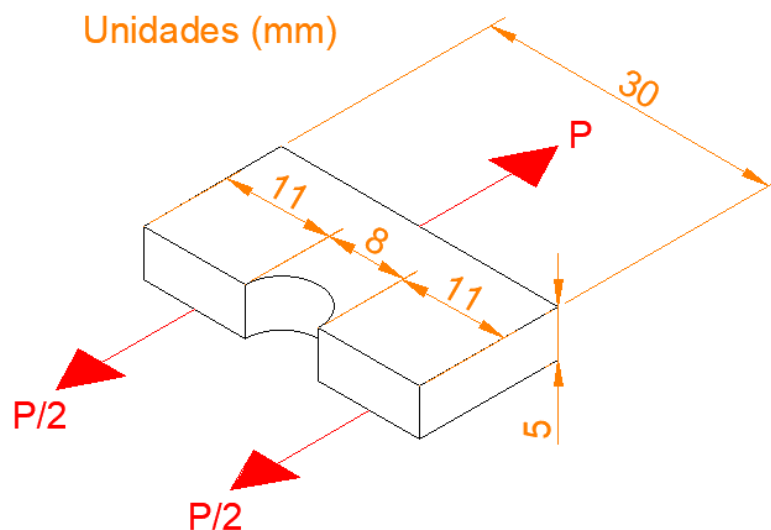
Esquema para esfuerzo de tracción en placa. [Autor]
